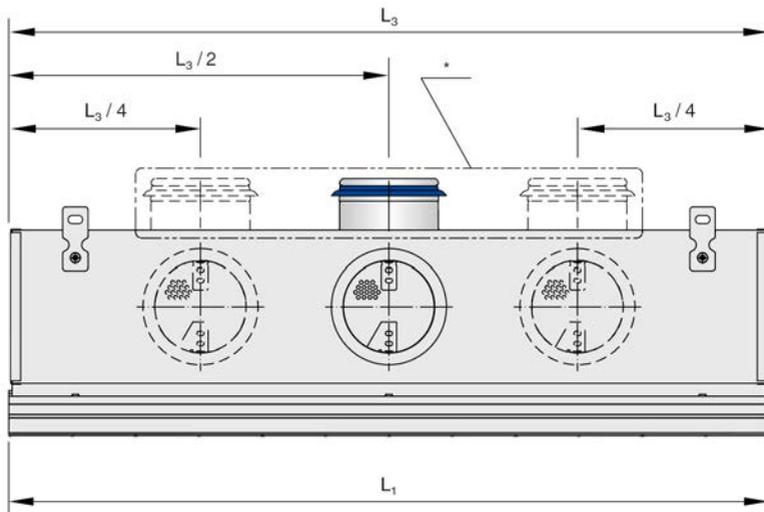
Размеры и расположение патрубков, * расположение патрубков для конструкции типа VS
